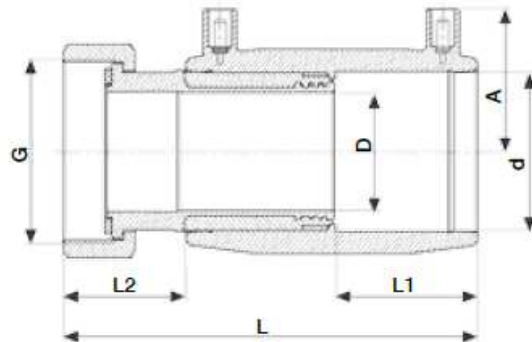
Plasson: Male transition Coupler – Corte longitudinal.
